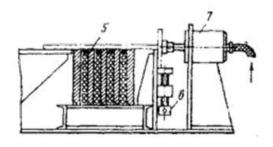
Пневмоэлектромагнитный прижим кондуктора для сварки тавровых балок.
